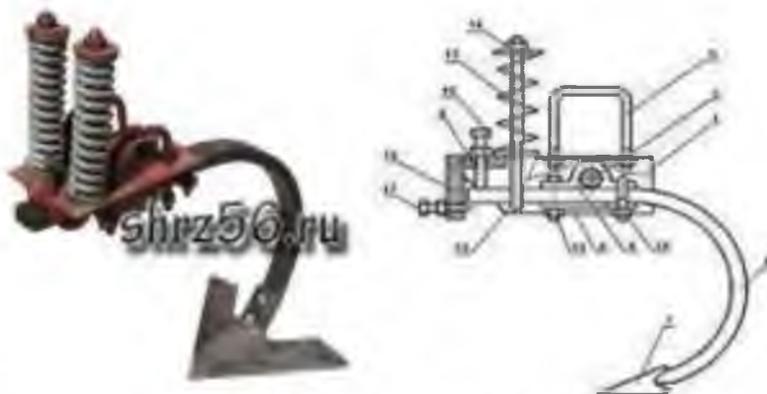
Пружні S-подібні стійки з індивідуальними пристроями регулювання
